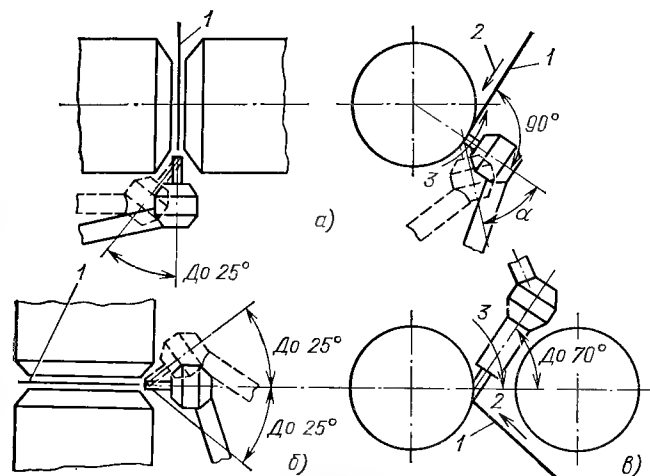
Взаимное расположение горелки и присадочной проволоки при ручной аргодуговой сварке неповоротных стыков труб.
